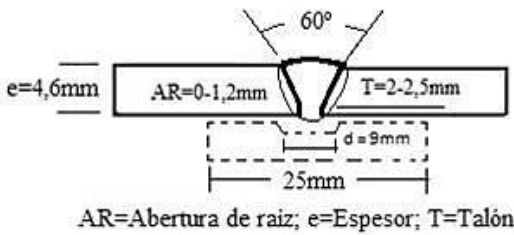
Diseño de junta a tope para las soldaduras de la aleación AA5083-H116 de una sola pasada.
